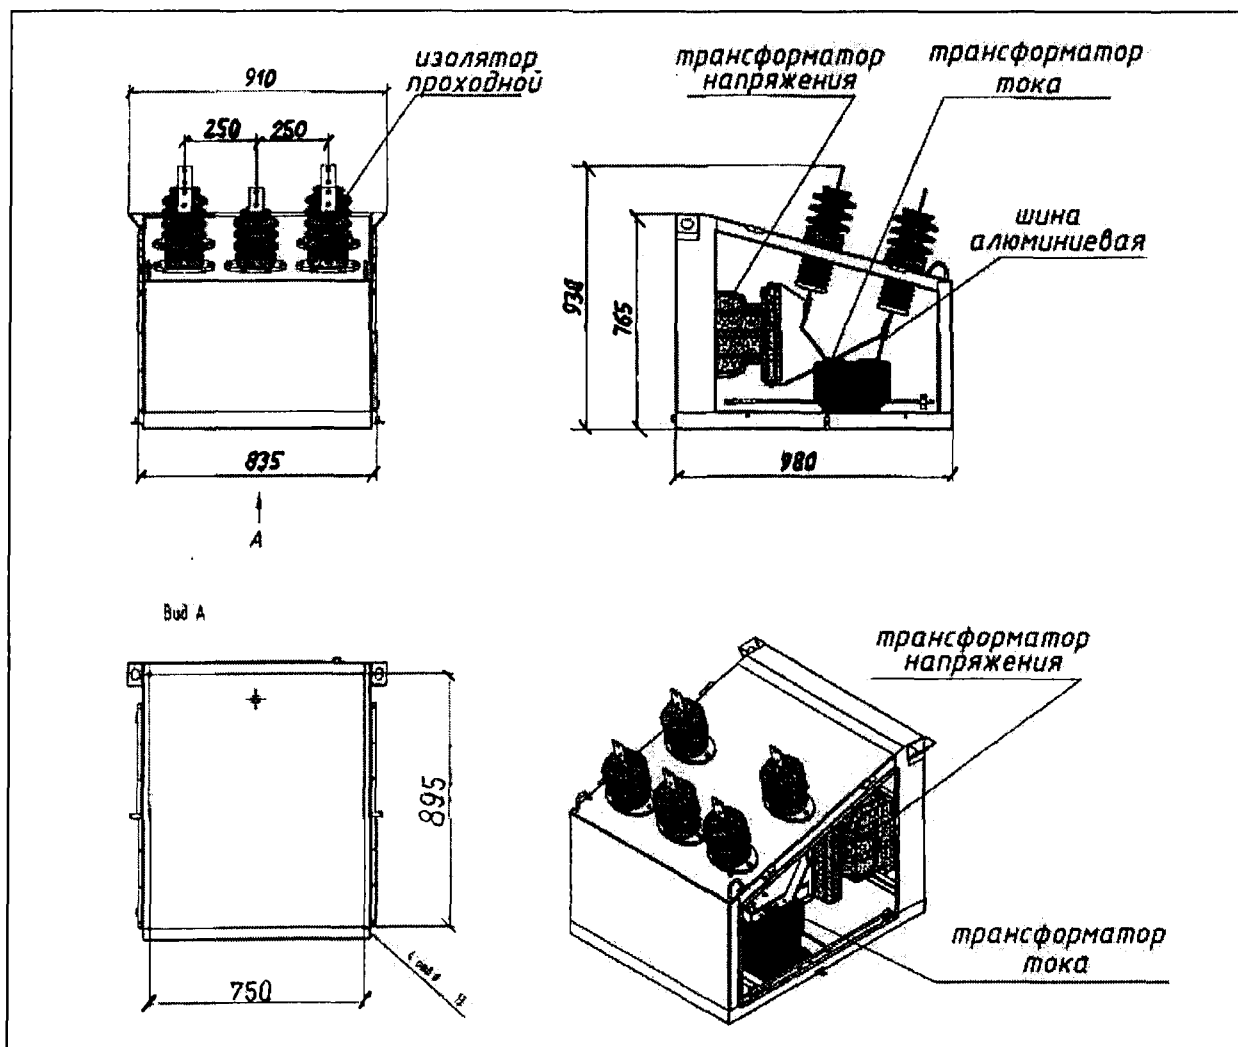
Габаритные и присоединительные размеры высоковольтного модуля
